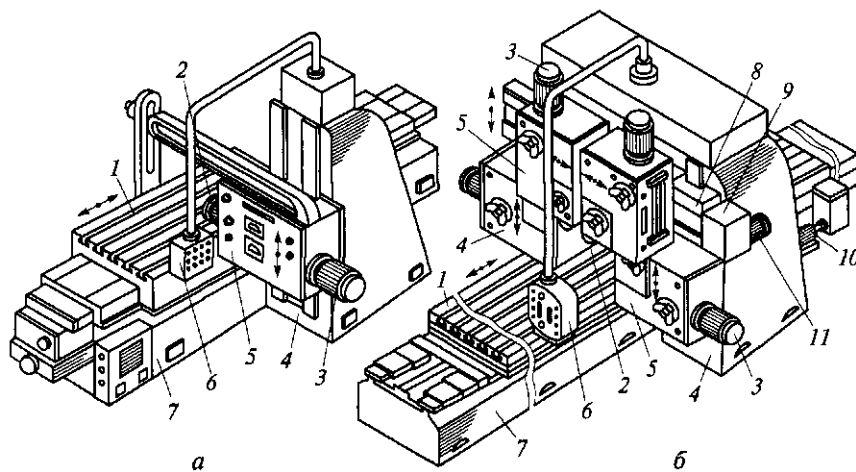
Одностоечный (*a*) и двухстоечный (*б*) продольно-фрезерные станки с ручным управлением:
